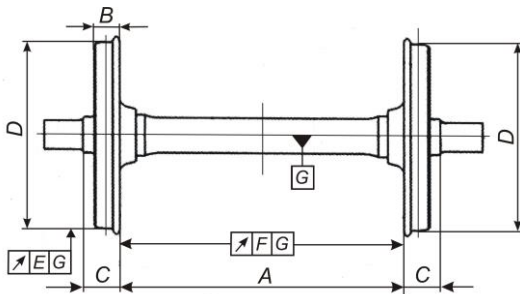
Колесная пара (без букс, дисков и редуктора) с основными размерами:
